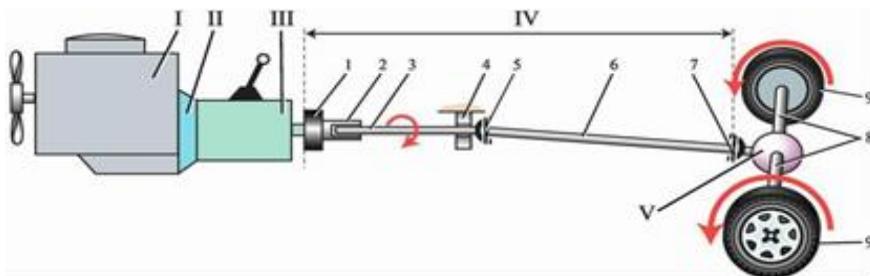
Схема трансмиссии заднеприводного автомобиля: I – Двигатель; II – Сцепление; III – Коробка передач; IV – Карданная передача: 1 – эластичная муфта; 2 – шлицевое соединение; 3 – передний карданный вал; 4 – подшипник подвесной; 5 – передний карданный шарнир; 6 – задний карданный вал; 7 – задний карданный шарнир; V – Задний мост с главной передачей и дифференциалом: 8 – полуоси; 9 – ведущие (задние) колеса
